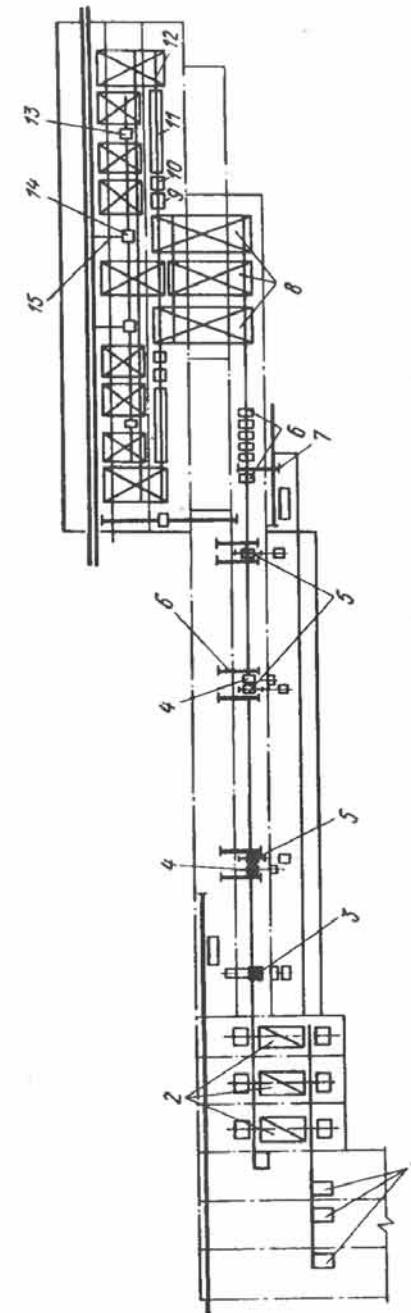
Схема расположения оборудования универсального балочного стана 1300:
